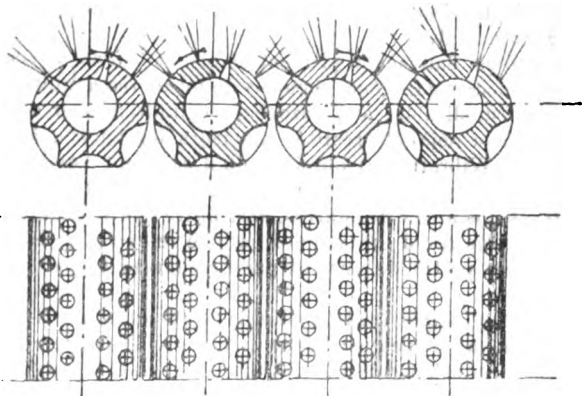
et 2. — Coupe et vue en plan d'une grille Sauvageot à quatre rouleaux.
